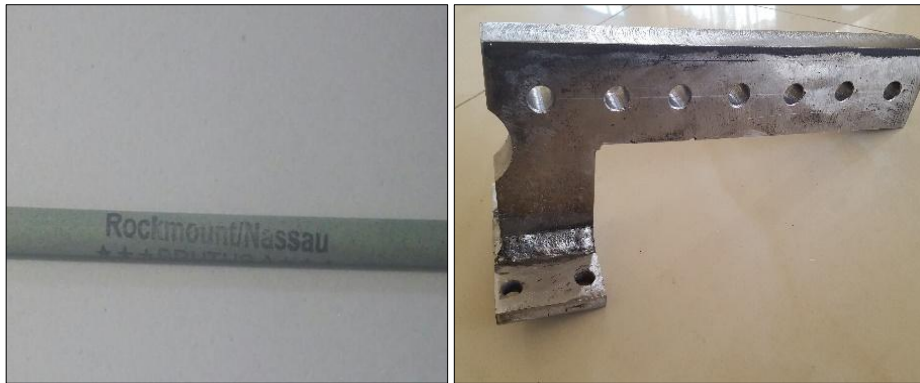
Electrodo y partes de la herramienta soldada
